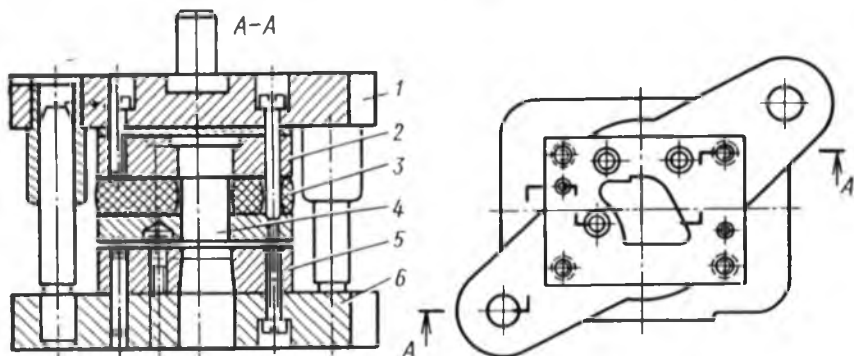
Стандартный вырубной штамп с верхним прижимом заготовки
